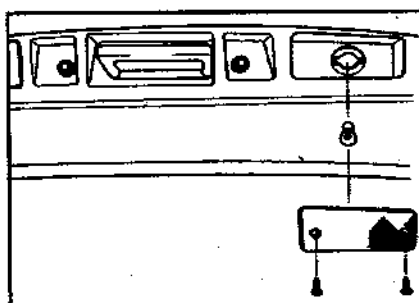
Расположение болтов крепления стекла фонаря освещения номерного знака
